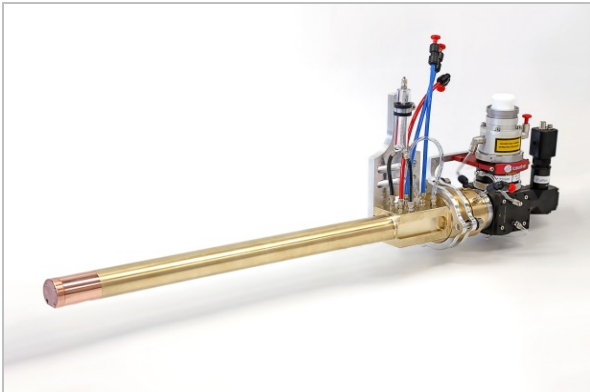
Ab einem Öffnungsdurchmesser von 30 Millimetern kann Pallas mit der iClad® -Innenbearbeitungsoptik das gesamte Spektrum der Innenkonturbearbeitung bis in 500 Millimeter Tiefe porenfrei beschichten.
